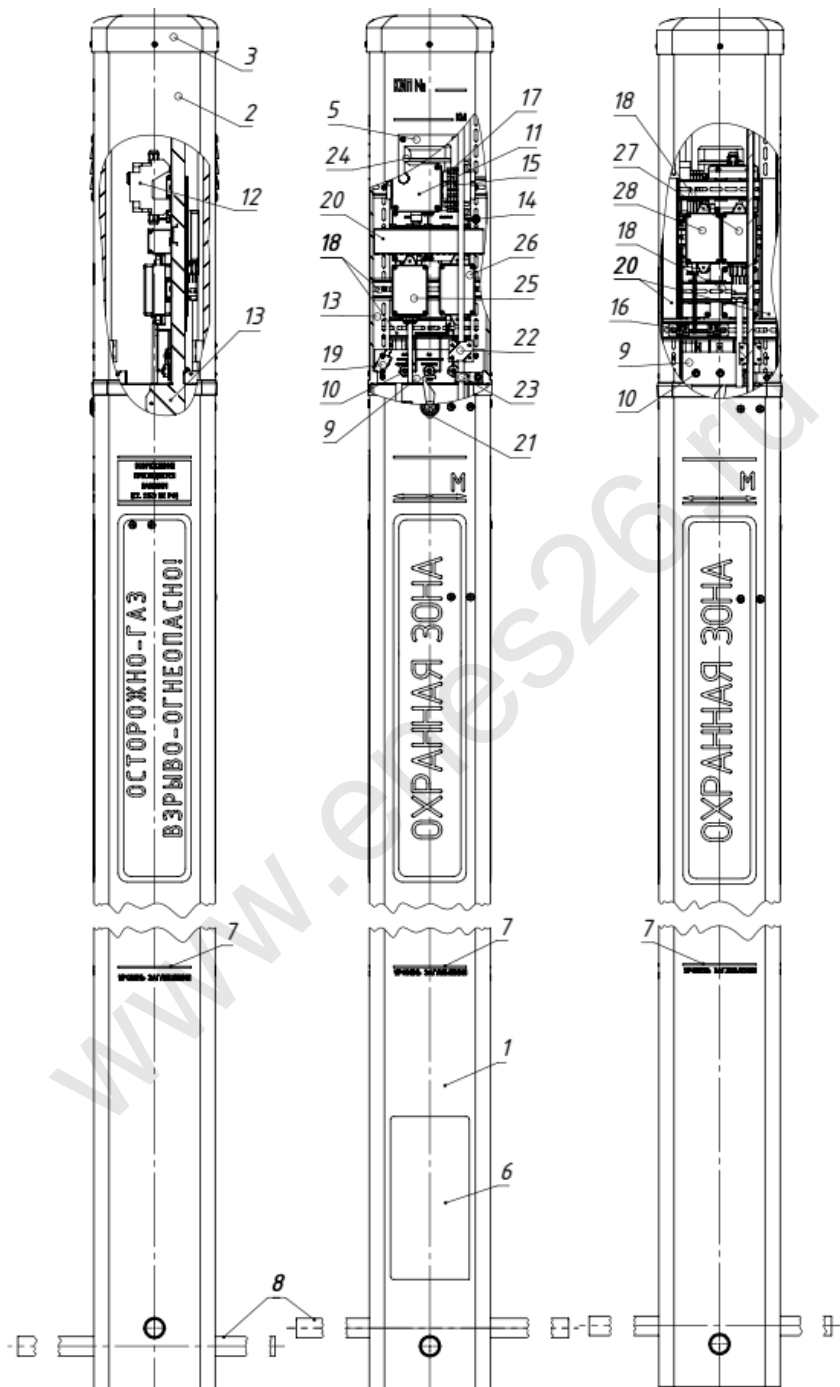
Общий вид ЗГАНС® УКМ-КИП
